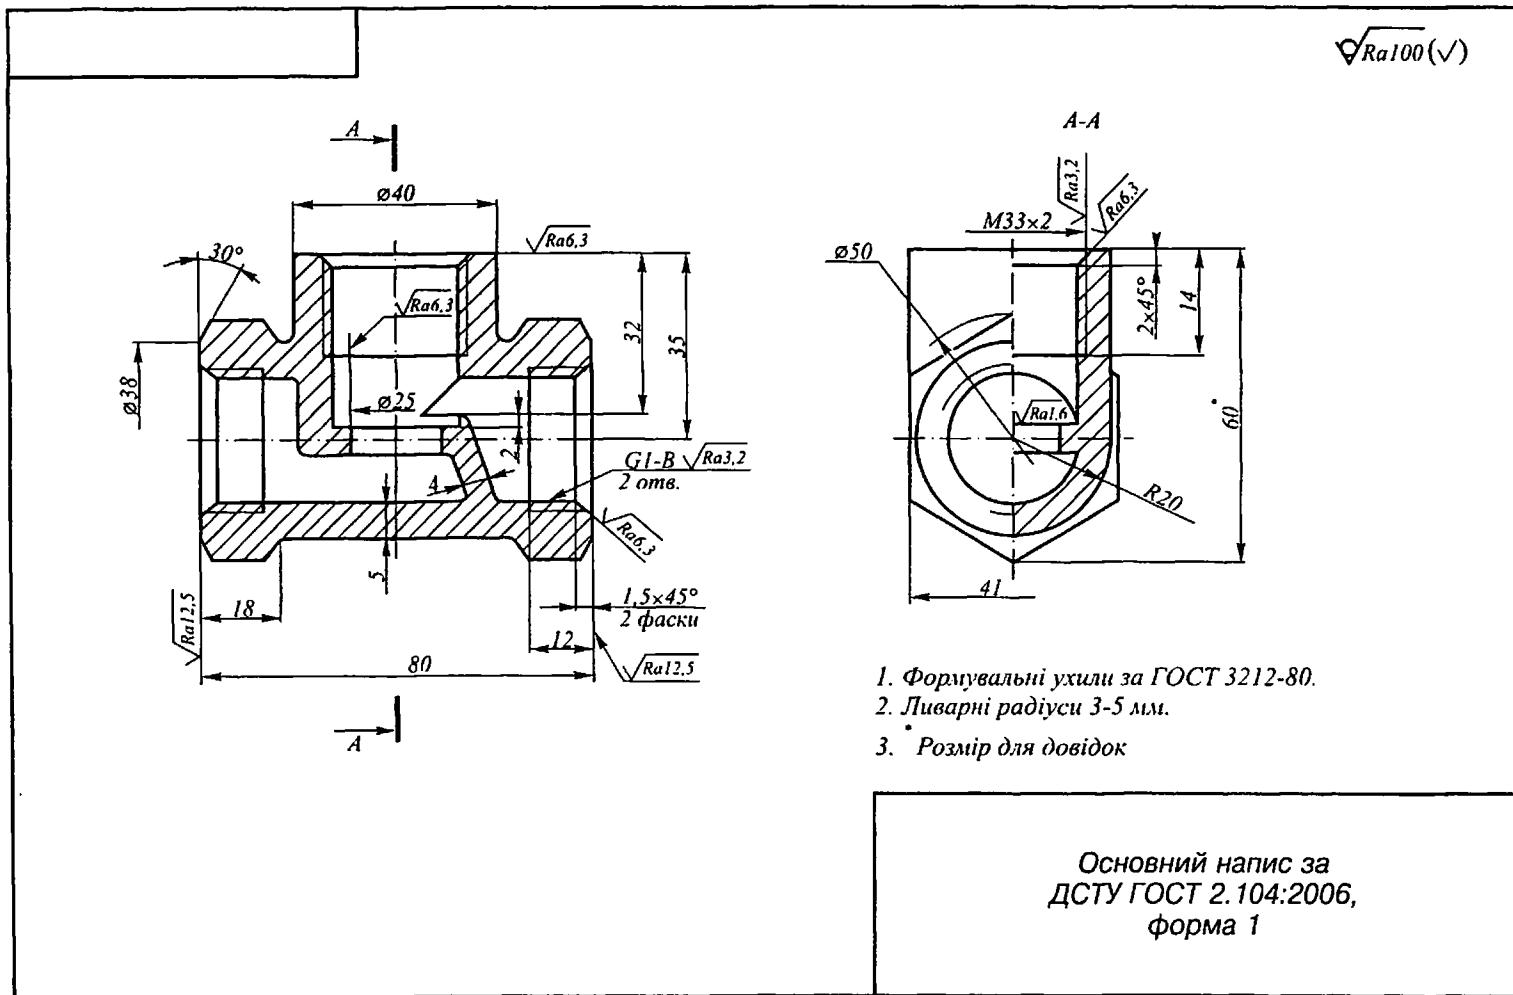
Приклад оформлення кресленника корпусної деталі, виготовленої з литої заготовки
